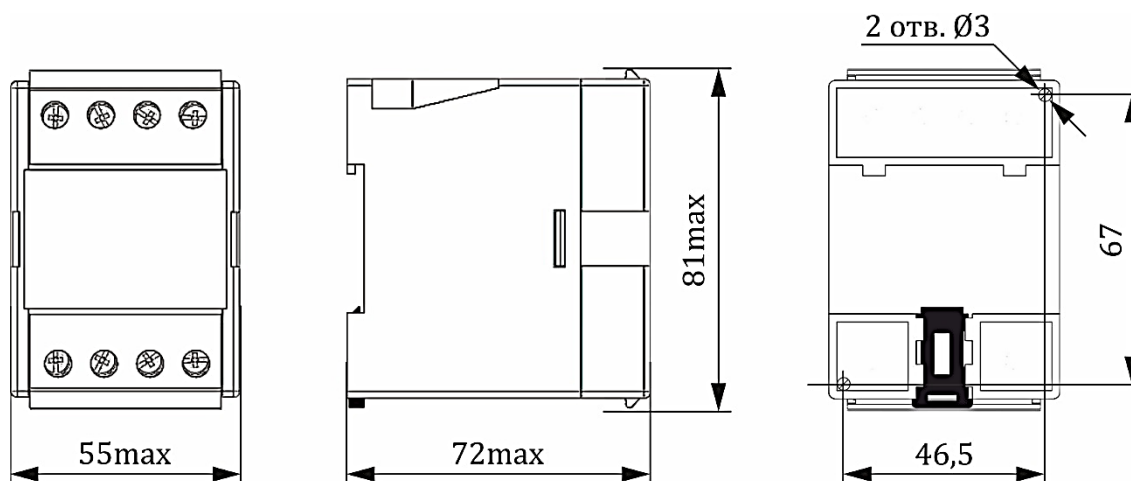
Габаритные и установочные размеры корпуса М8
